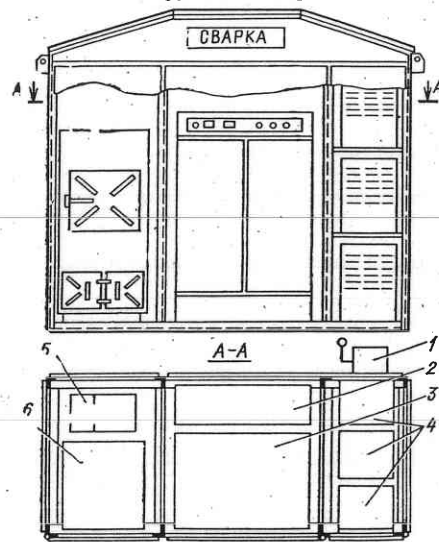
Инвентарная переносная установка для многопостовой сварки:
